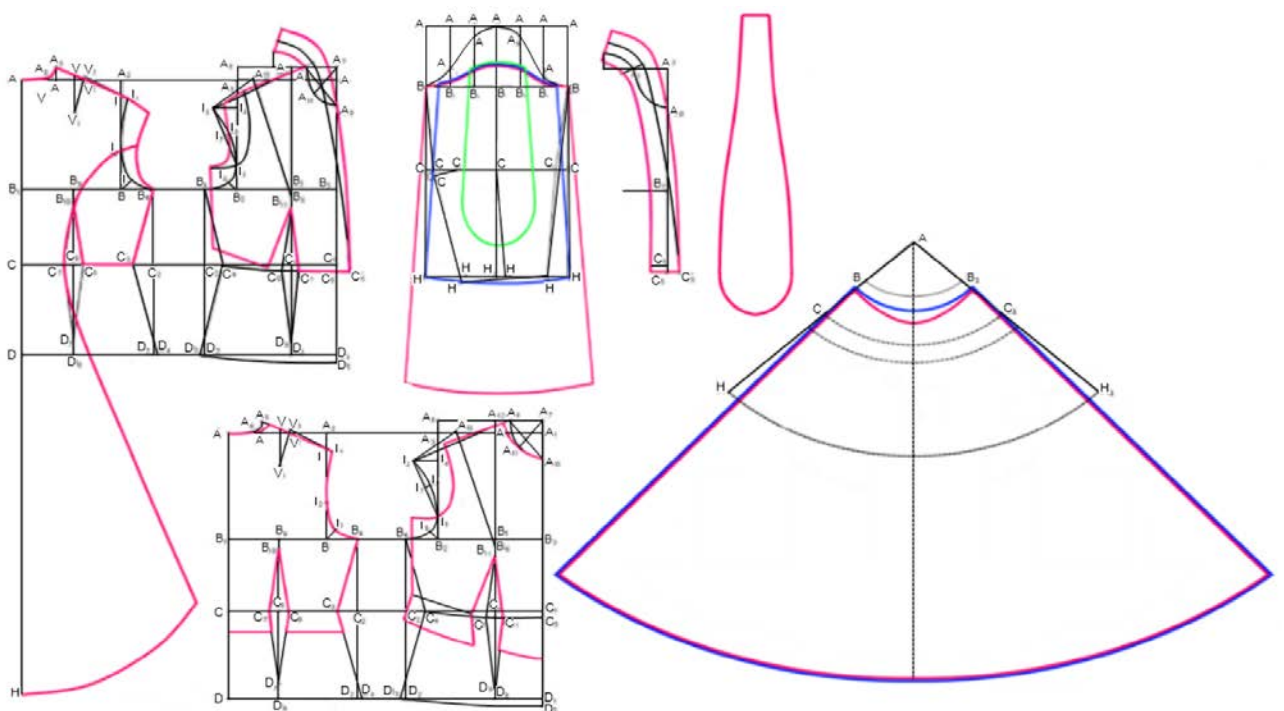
Конструктивный чертёж женского вечернего платья (модель 2)
